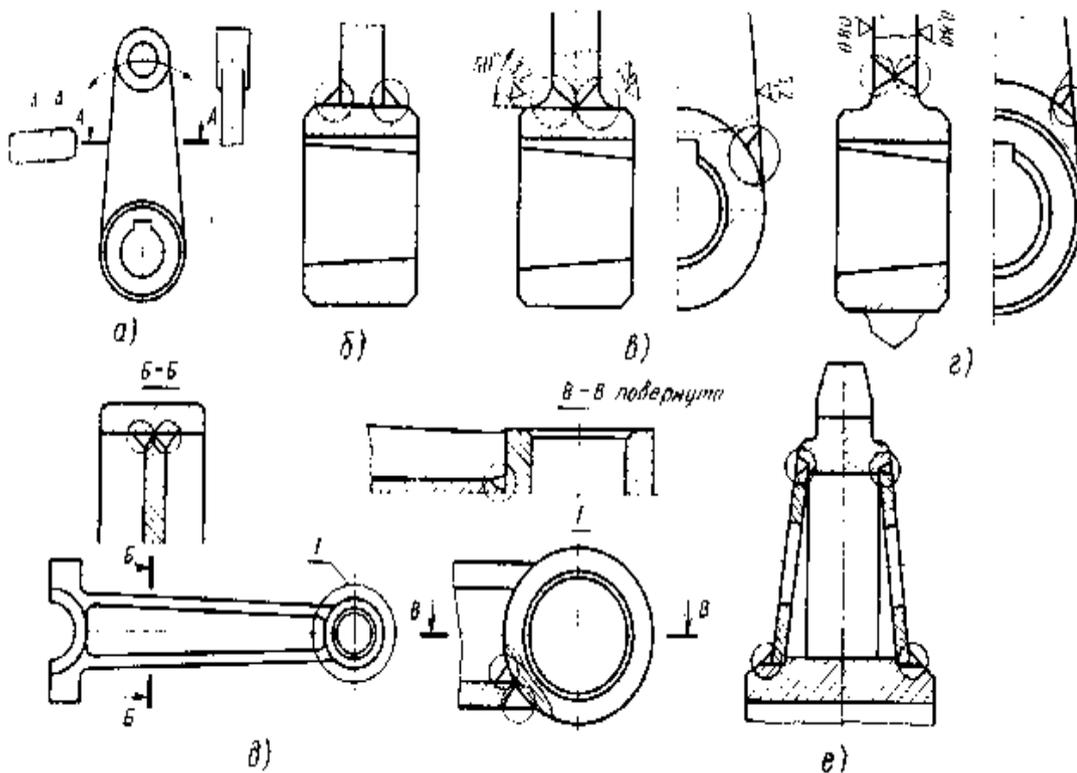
Сварные конструкции, работающие при переменных нагрузках
